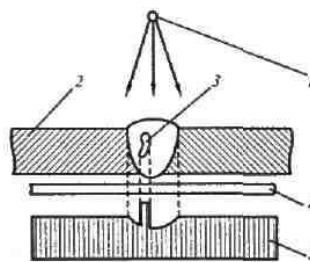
Схема просвечивания сварного соединения:
